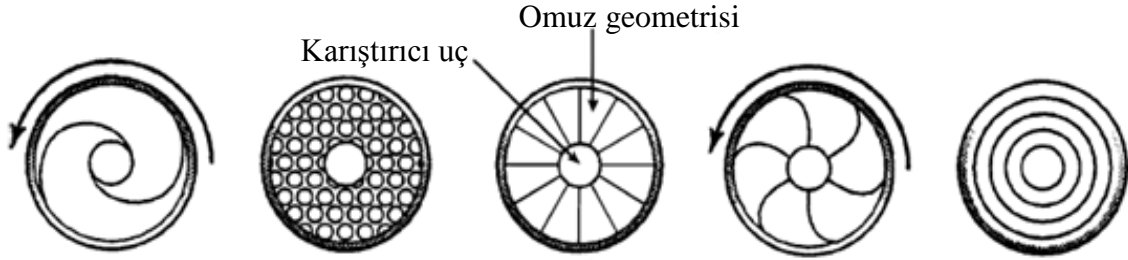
SKK kaynak takımı karıştırıcı uç kısmı geometrilere ait örnekler [49].
